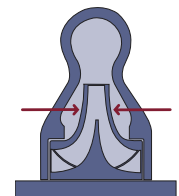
Ausgleich des Axial Schubs durch zweiflutiges Laufrad
